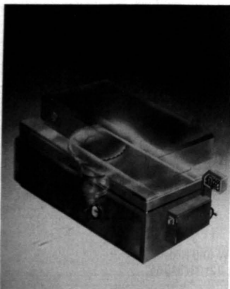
Dickenfräsmaschinen (Bildnachweis: Lestro)
